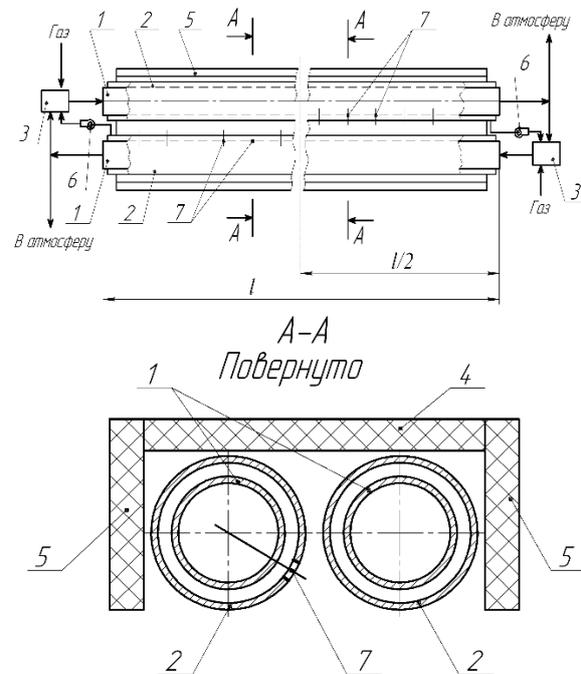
Схема нового ленточного газового инфракрасного нагревателя с двойным теплоизлучающим контуром: 1 – основной трубный излучатель; 2 – рабочий трубный излучатель; 3 – газогорелочный блок; 4 – верхняя панель теплоизоляции; 5 – боковая панель теплоизоляции; 6 – вентилятор; 7 – отверстия в рабочем трубном излучателе.
